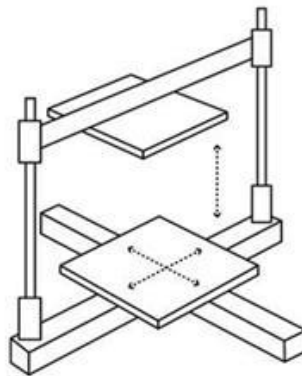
Impresora 3D Cartesiana. Imagen extraída de <http://tecnoimpre3d.com/delta/>.
